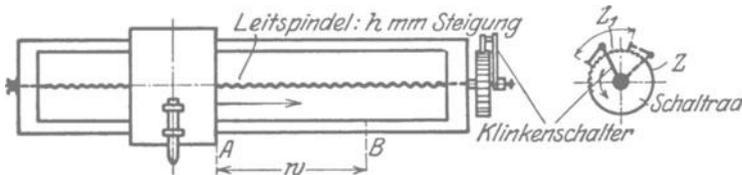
u. 14. Vorschub des Werkzeugschlittens.
